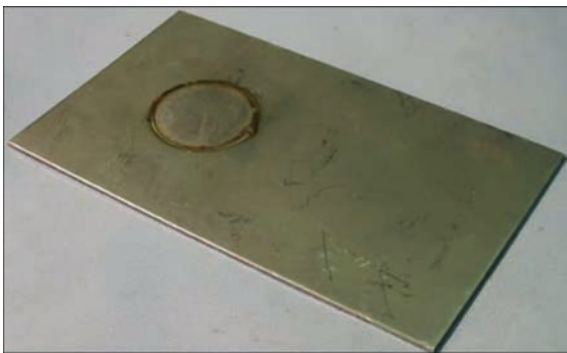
Диск зі сталі ODS, вварений в пластину з нержавкюї сталі
